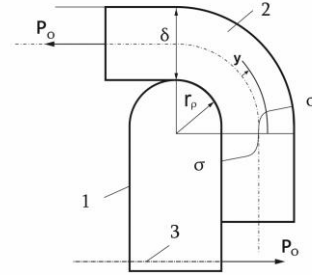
Схема огибания ролика листовой заготовкой: 1 – ролик; 2 – листовая заготовка; 3 – ось вращения обкатного ролика
